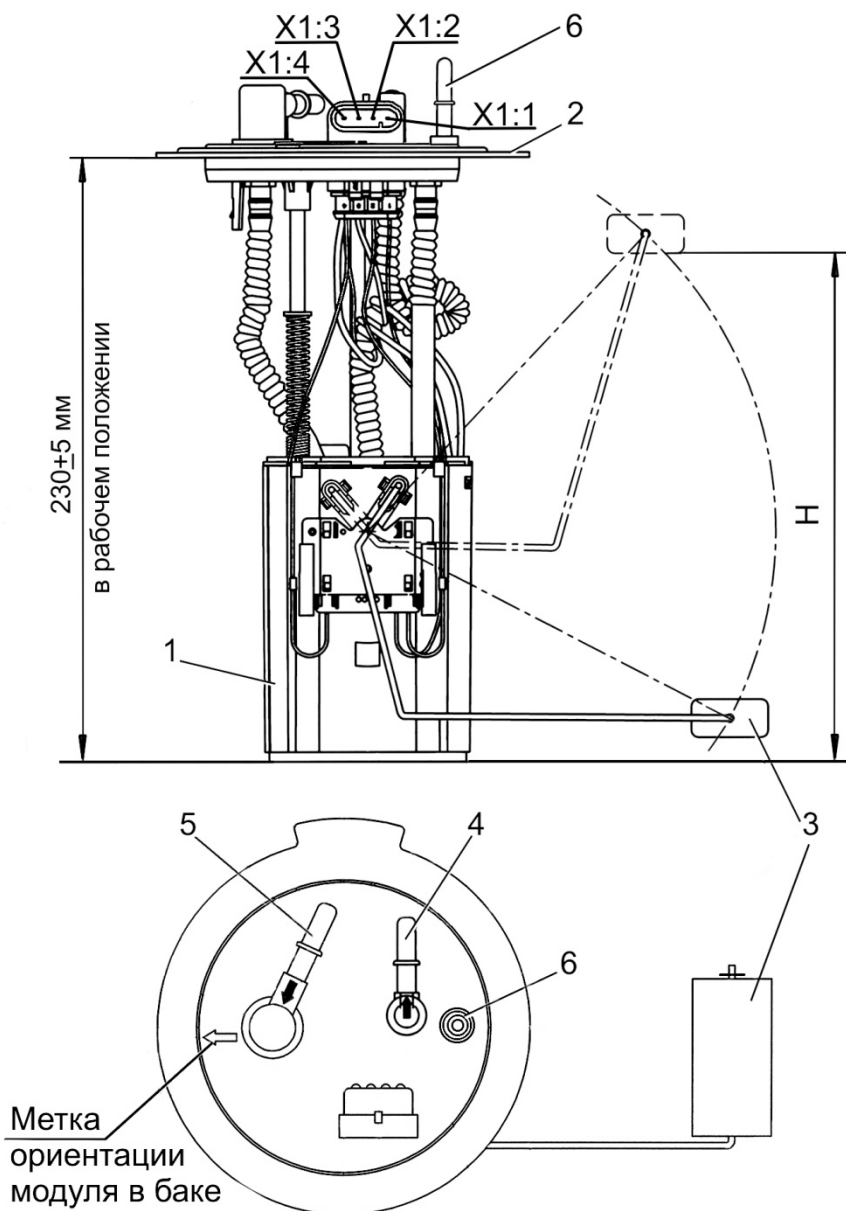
Модули топливозаборников: Н - положение поплавка; 1 - противоотливной стакан; 2 - кольцо прижимное; 3 - поплавок датчика уровня топлива; 4,5,6 - штуцеры
